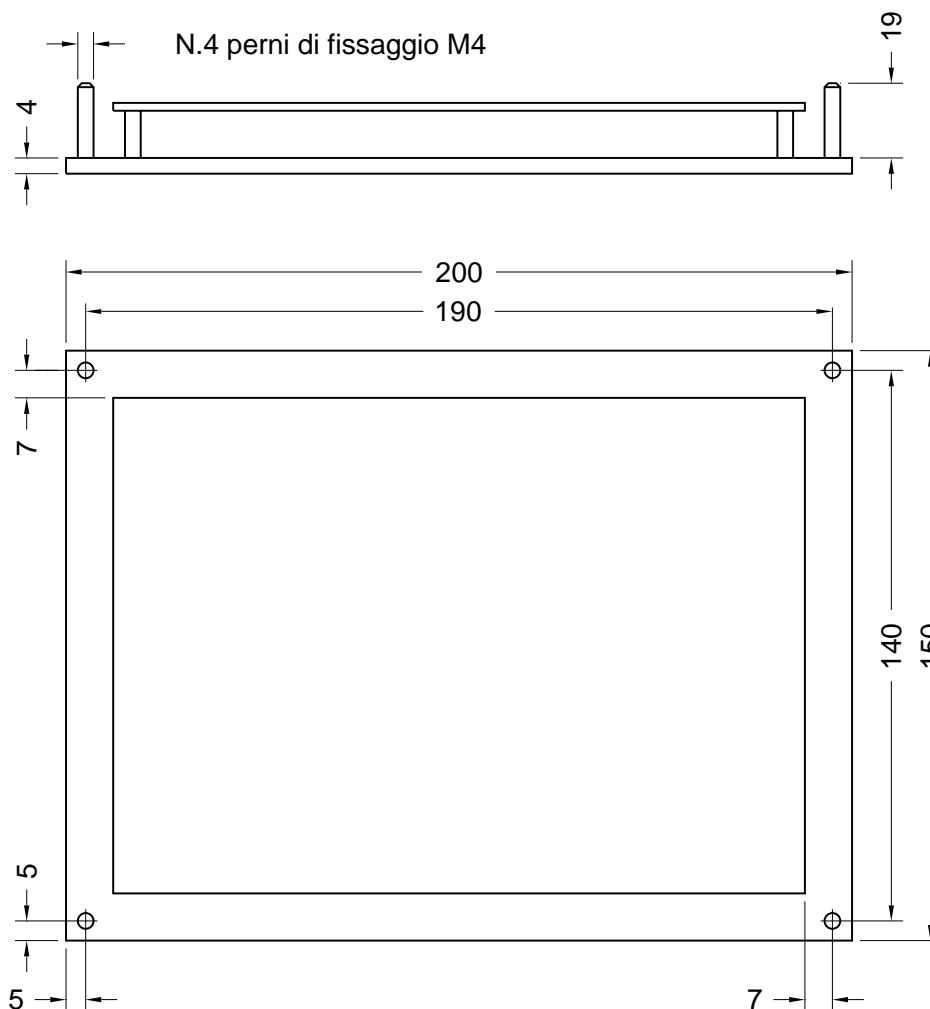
Dimensioni e fissaggio del terminale slave PTD2SC
